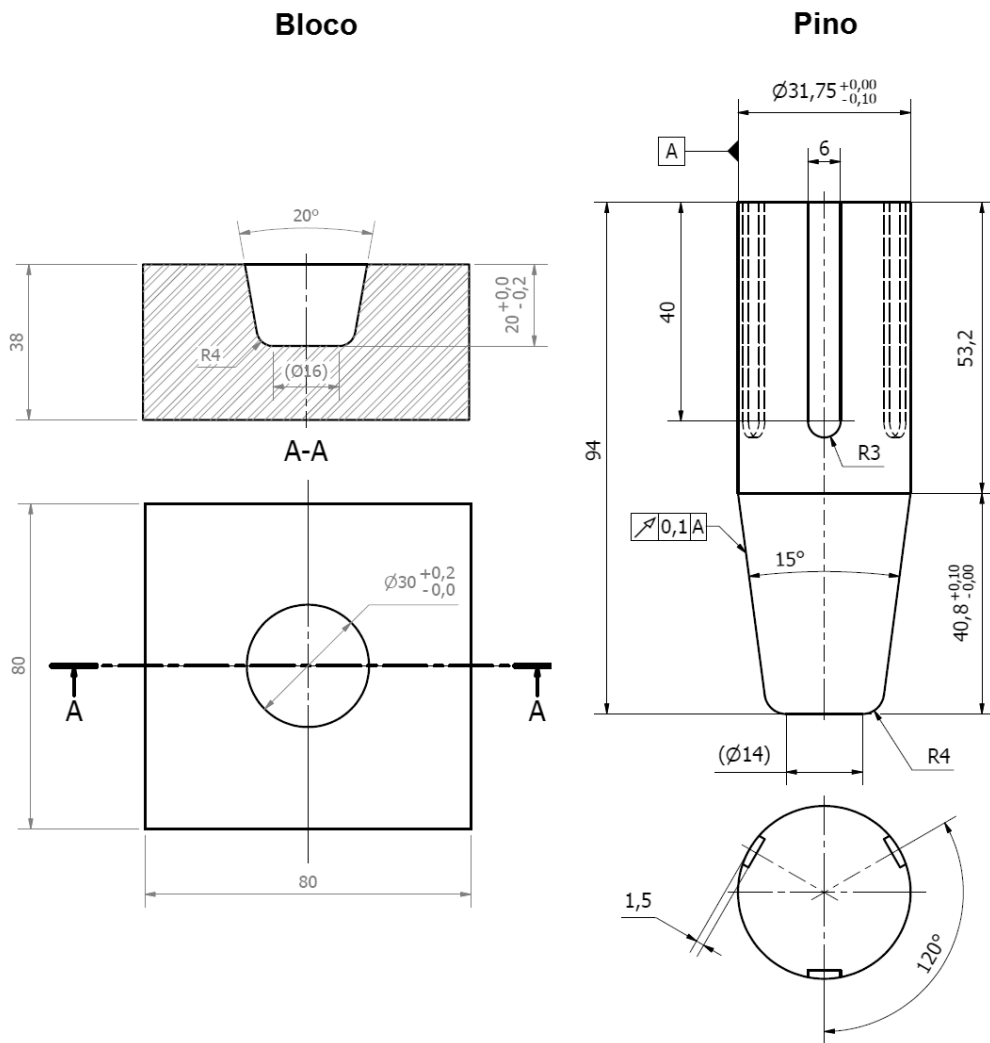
Dimensões do pino e do bloco da geometria “B” (cotas em mm)
